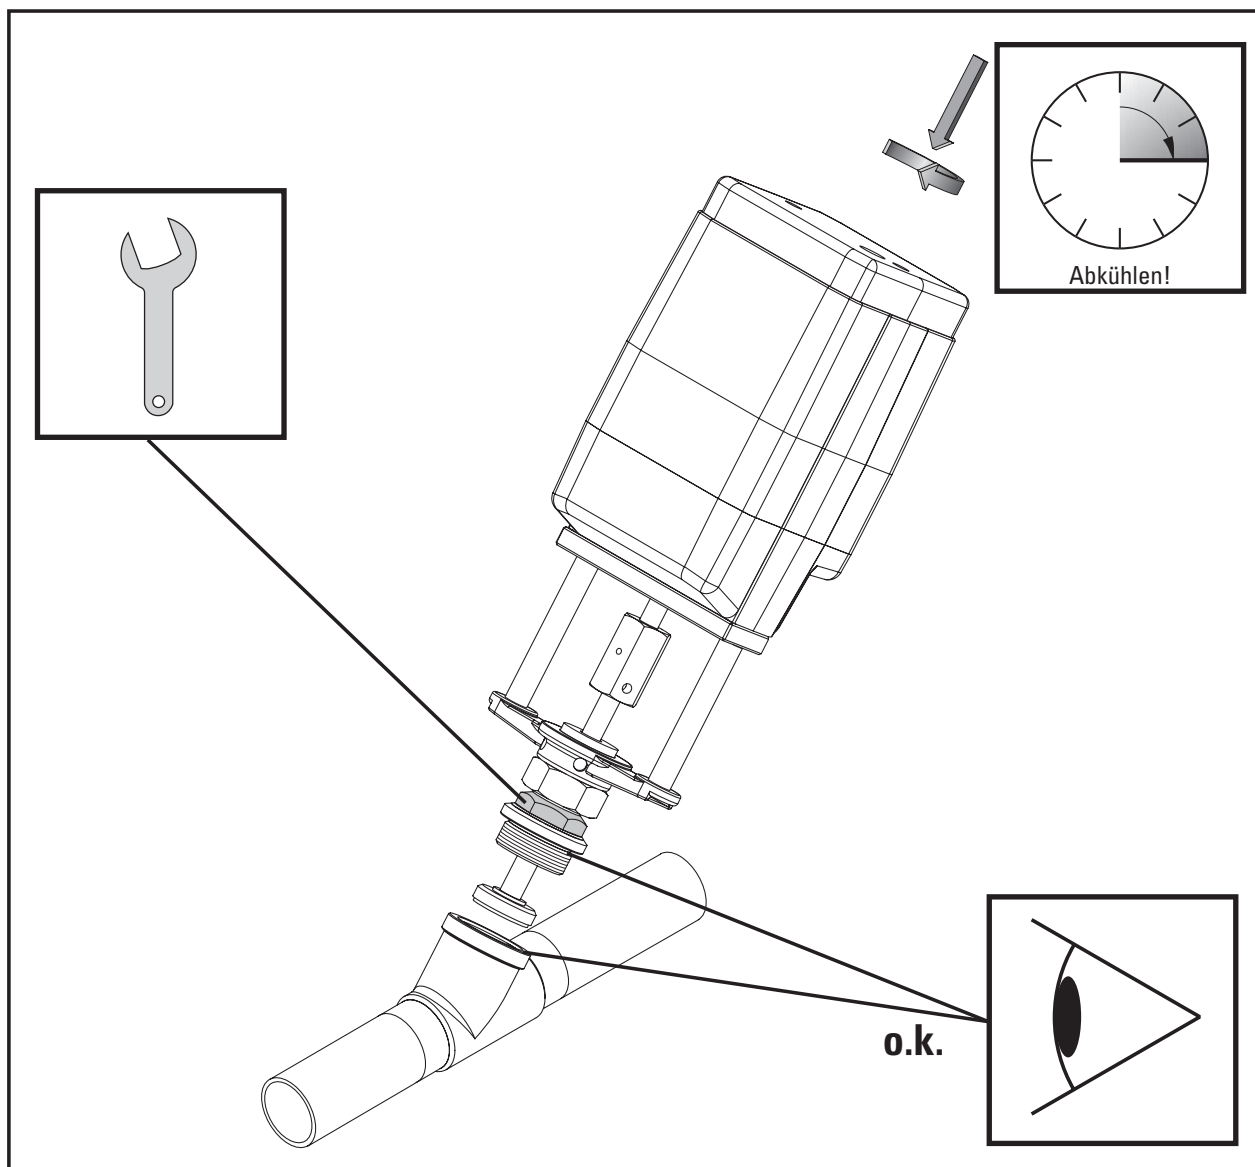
Montage des des Einschraubteils mit Antrieb
